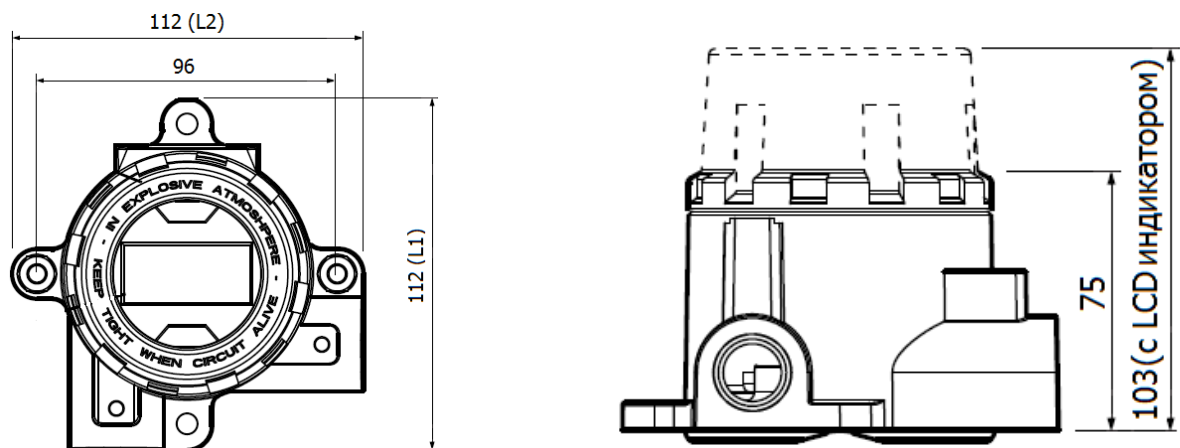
Соединительные головки J5, J6, J7, J8 для ДТ 644
